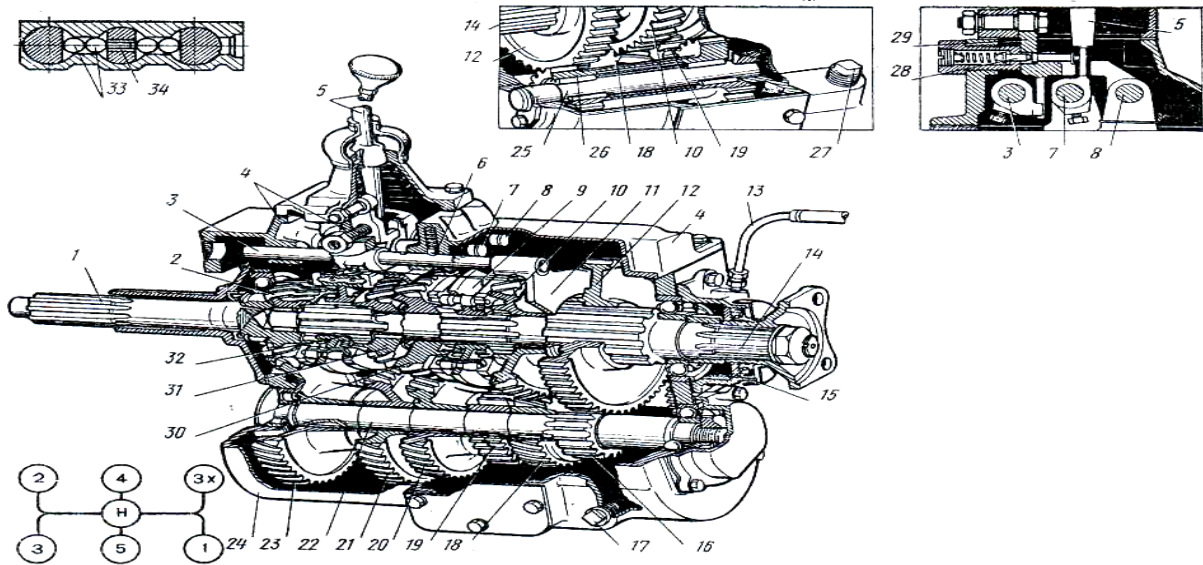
Коробка передач автомобіля ЗІЛ-131
